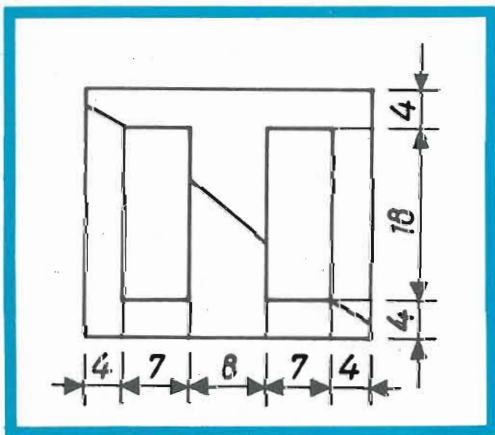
Dimensioni dei lamierini del trasformatore bloccato.
